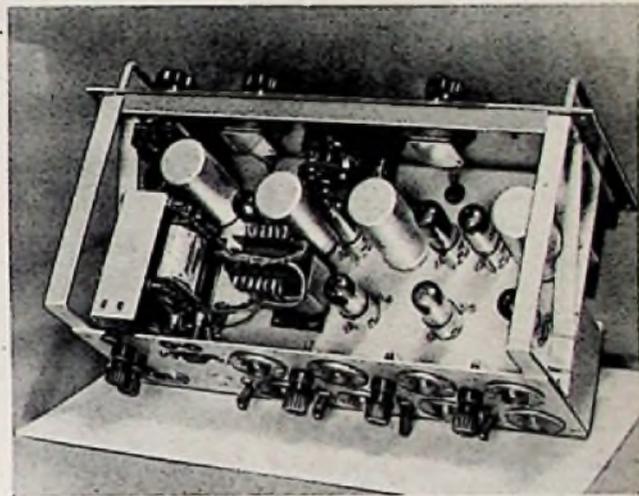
Zusammenbau des Chassis mit Front- und Anschlussplatte
